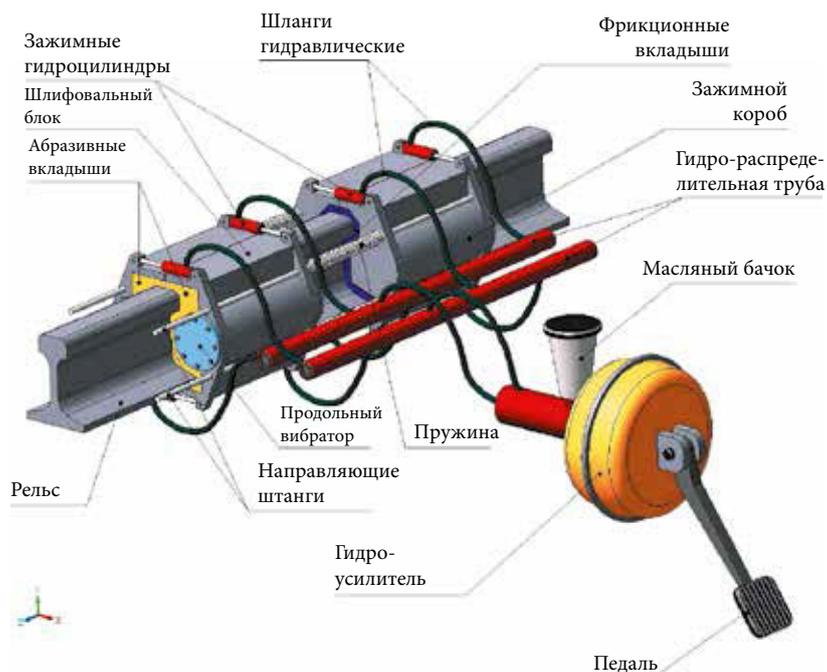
Схема устройства для шлифовки рельсовых стыков после стыковой сварки. Рычажно-гидравлическая система шлифовального устройства
